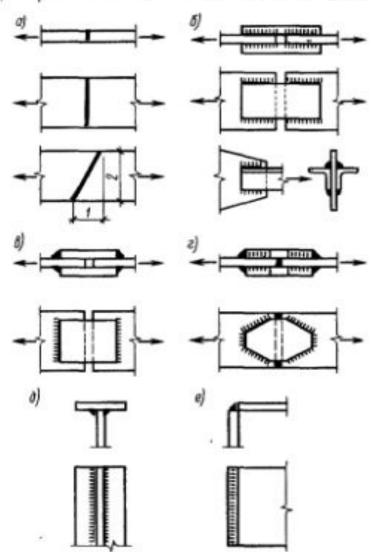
Виды сварных соединений: а — стыковое; б — внахлестку фланговыми швами; в — то же, лобовыми швами; г — комбинированное; д — впритык тавровое; е — то же, угловое
